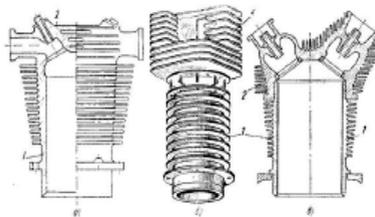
Цилиндры двигателей с воздушным охлаждением: а) моноблок; б) и в) составные цилиндры
